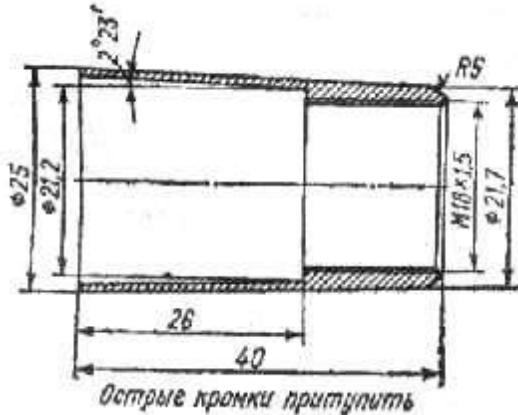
Приспособление для установки сальника левой цапфы коленчатого вала
